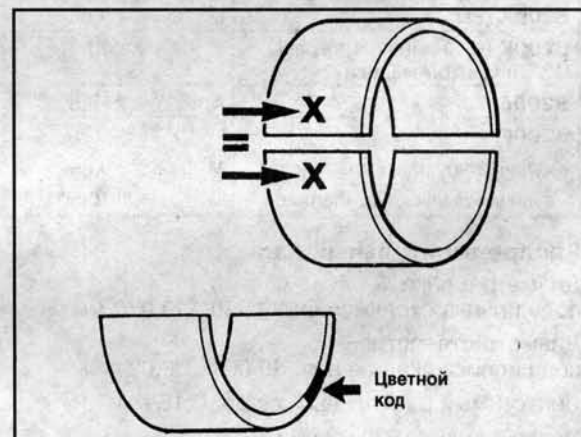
Обозначение полувыкладшей коренных подшипников
